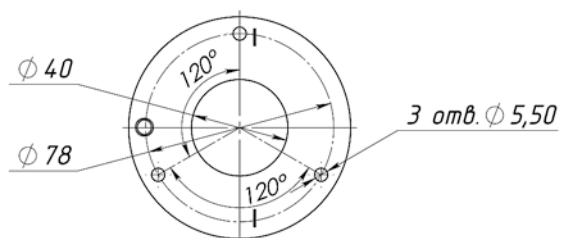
Разъединитель PE19-41(43)-72250-00 УХЛЗ на два направления с боковой смещенной рукояткой
